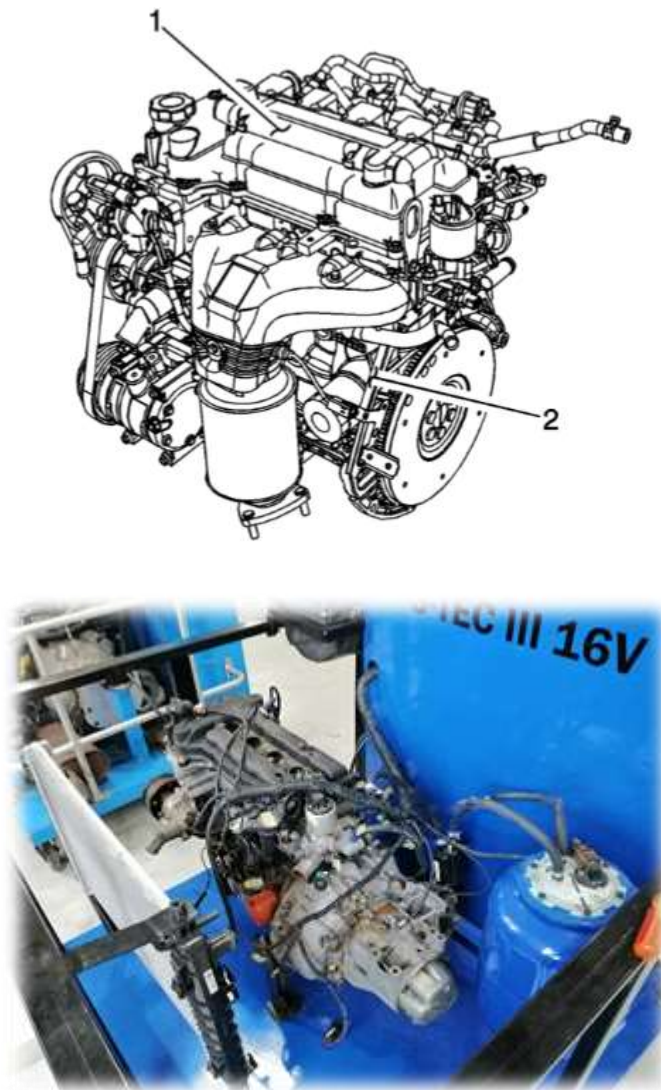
Motor Chevrolet S-TEC III 1.4L (G.M., 2012)
